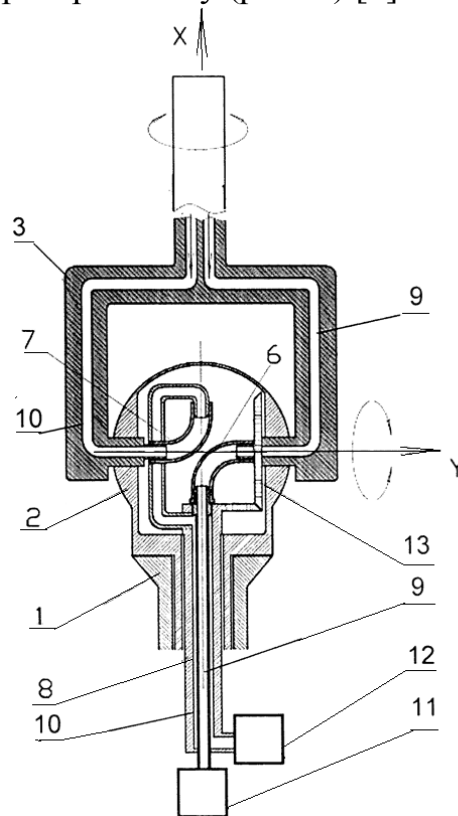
Датчик повітряної швидкості: 1 - корпус датчика; 2 - двовісний карданний підвіс; 3 - поворотна рама; 4 - приймач повітряних тисків; 5 – флюгер; 6 - перший гнучкий трубчастий елемент; 7 - другий гнучкий трубчастий елемент; 8 - коаксіальний трубопровід; 9 - пневмотраса повного тиску; 10 - пневмотраса статичного тиску; 11 - перший електричний перетворювач тиску; 12 - другий електричний перетворювач тиску, 13 - редуктор
